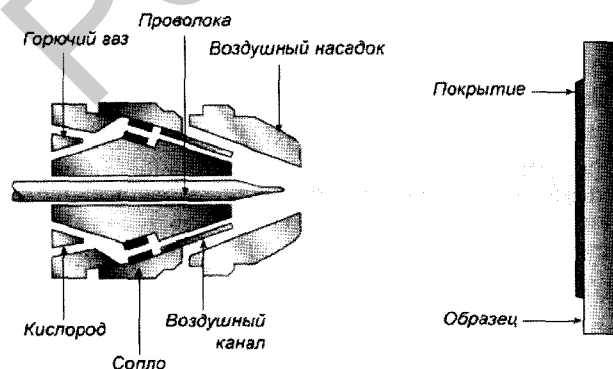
Схема процесса газопламенного нанесения покрытий распылением проволоки
